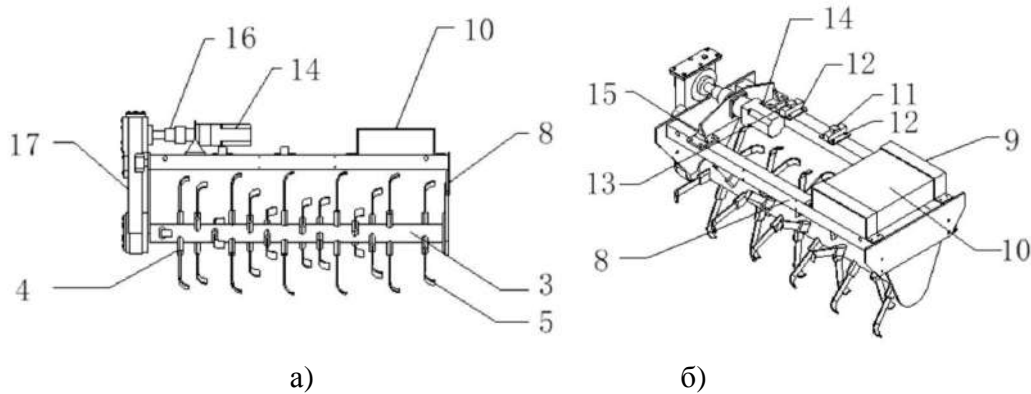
Общий вид роторного культиватора с приводом от электродвигателя:
